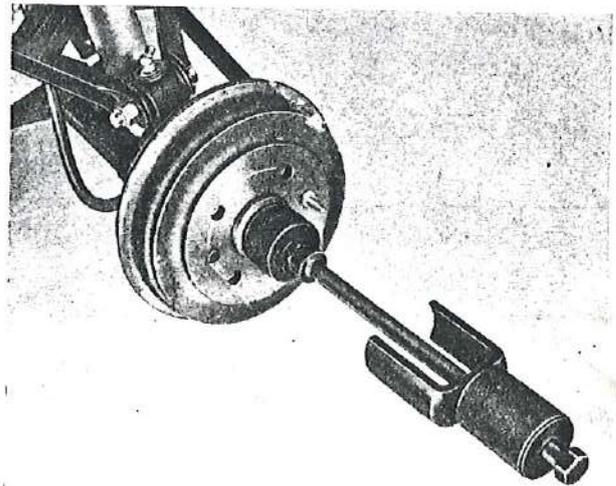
Montaje de la cazoleta buje rueda anterior derecha, mediante el útil A. 66008.
